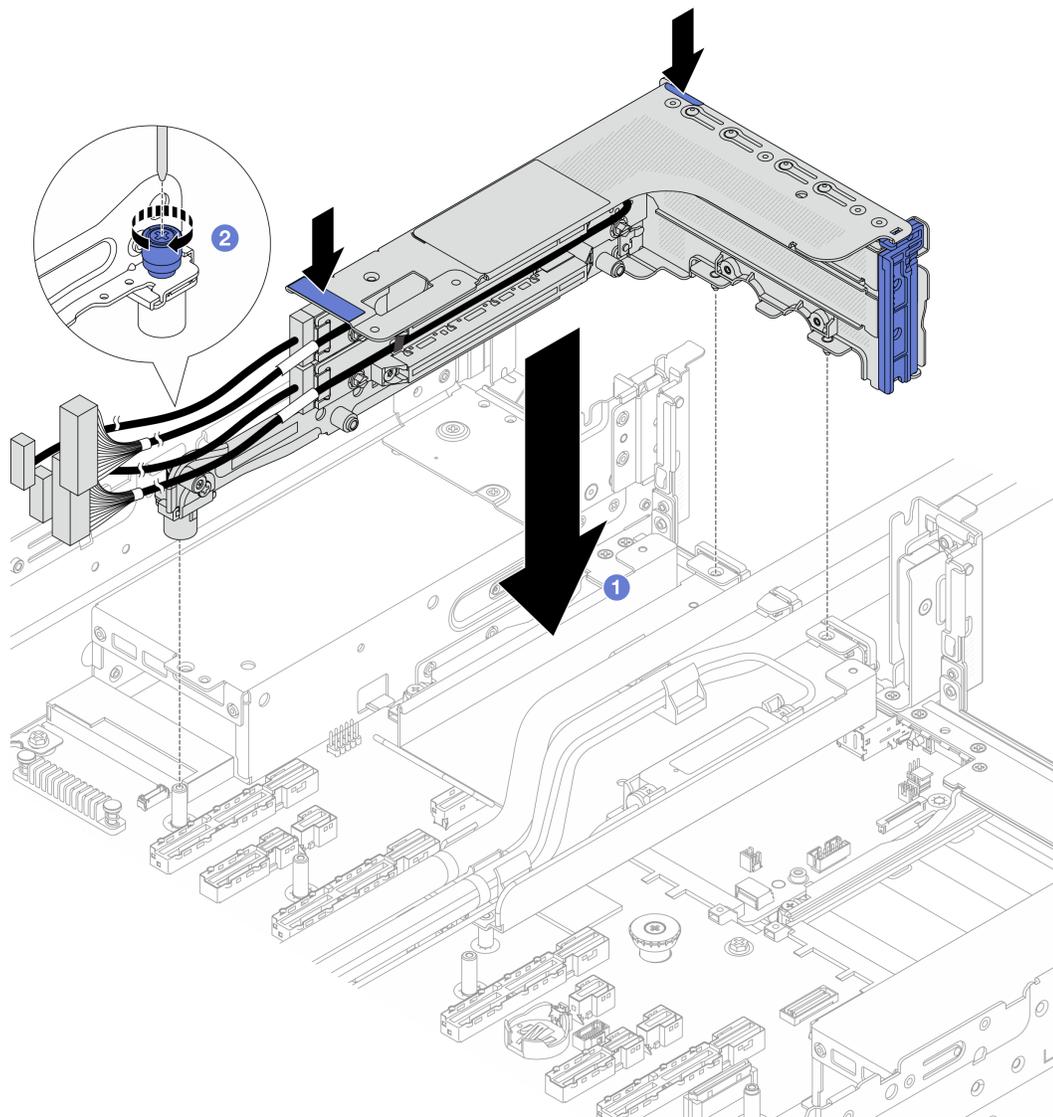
Установка отсека платы-адаптера Riser 3FH
